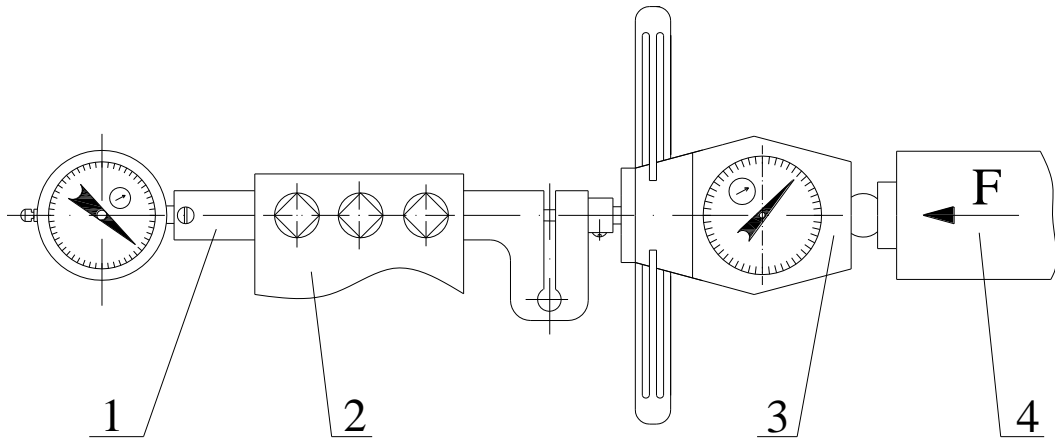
Схема тарування державки вигладжувача: 1 – державка з індикатором годинникового типу; 2 – різцетримач токарного верстату; 3 – динамометр стискування зразковий механічний ДОСМ-3-0,05; 4 – задня бабка токарного верстату
